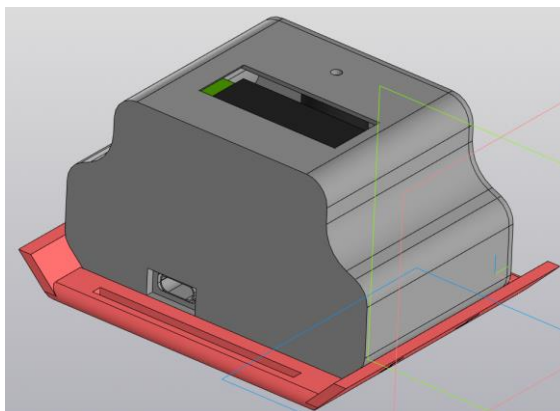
Остаточна компоновка механічної частини носимого пристрою
